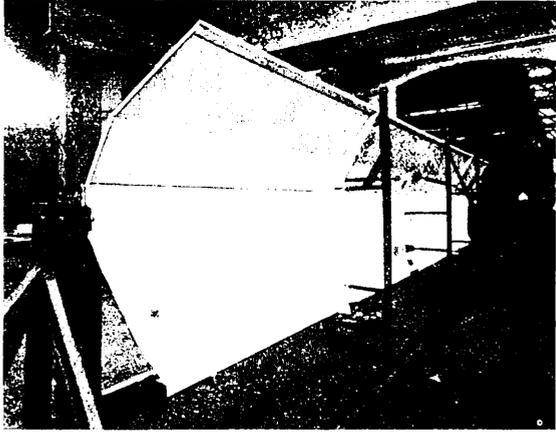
Seitenwand in der Schweißvorrichtung.
